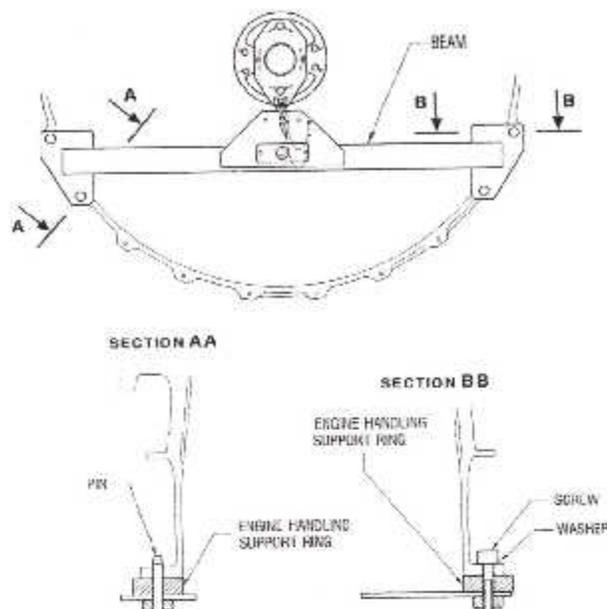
Installation du Beam (poutre), 856A3704G01.
